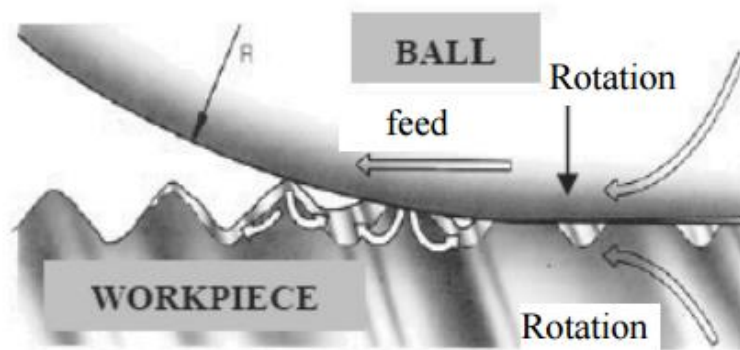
Механізм процесу розкочування поверхні [25]
